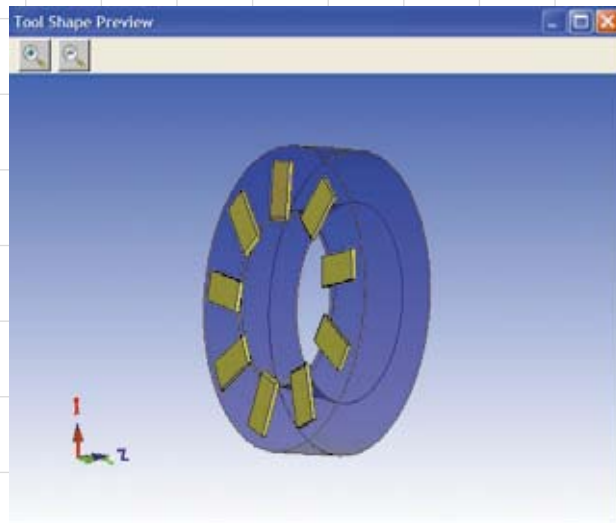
Инструмент для кольцевого вихревого фрезерования (Thread Whirling)
